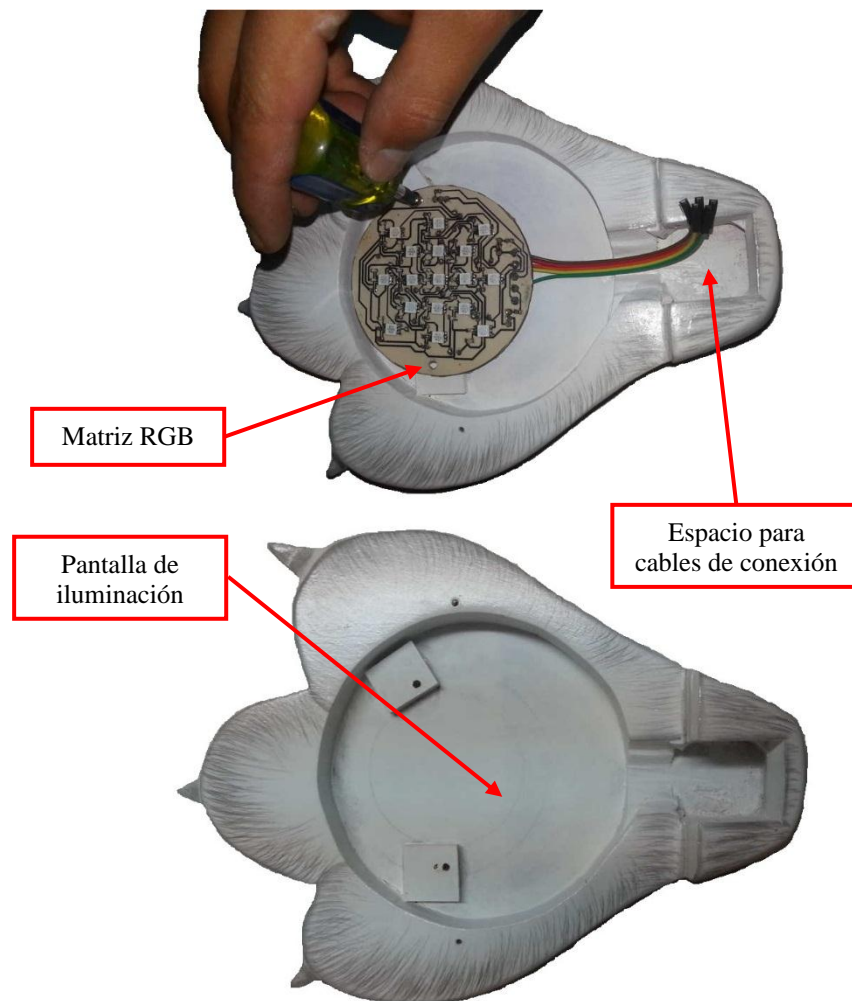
Diseño mecánico de la pantalla de iluminación
